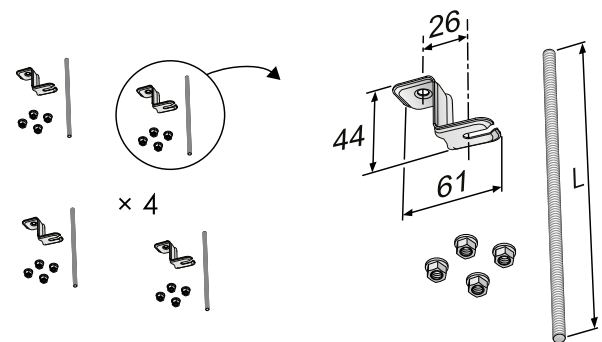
Élément d'assemblage SYST MS M8-1, montage au plafond et sur tige filetée
